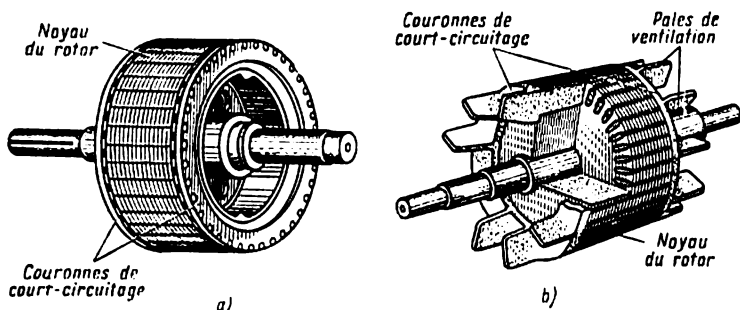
Vue extérieure et coupe partielle d'un rotor en court-circuit :
